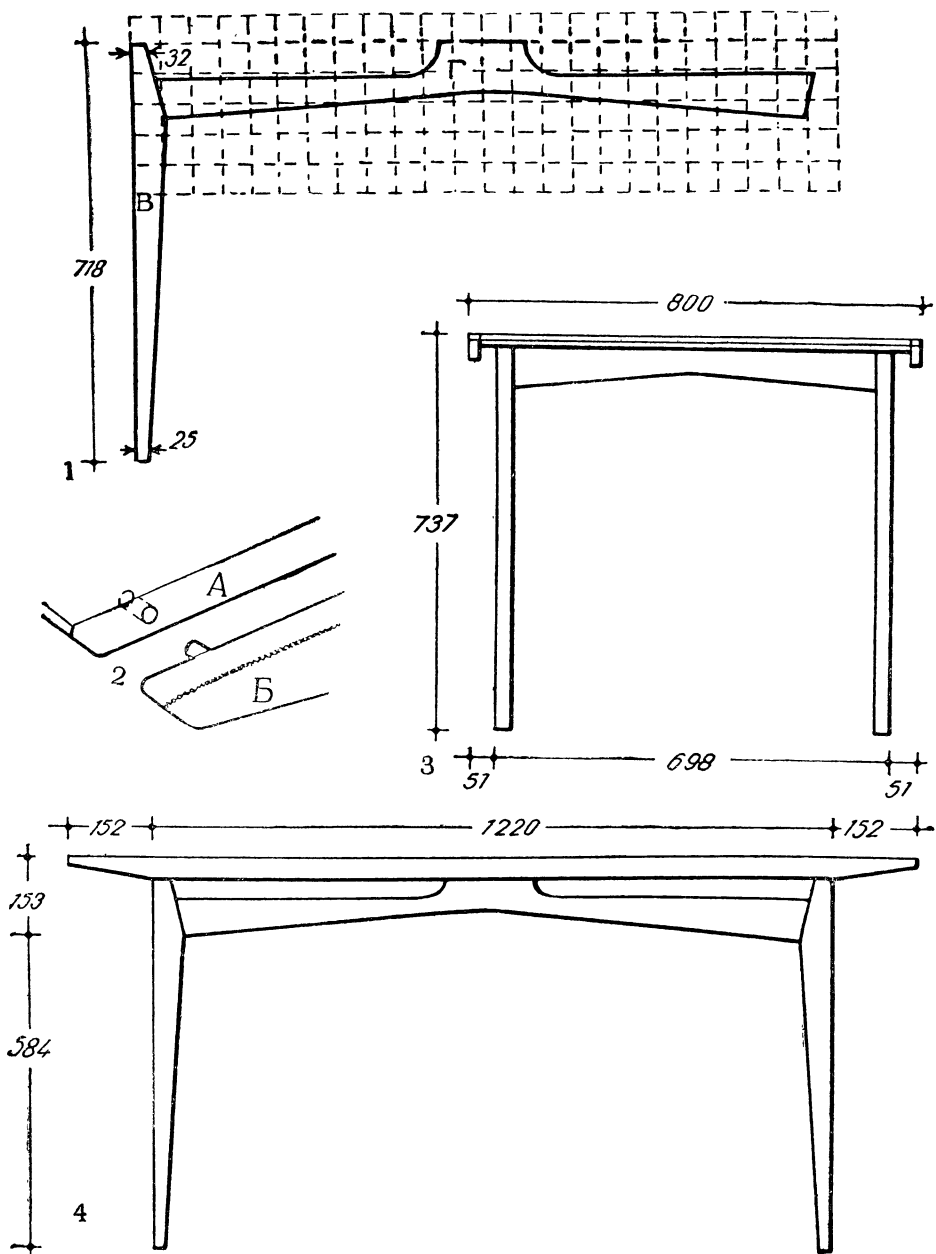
4. 1 — шаблон для изготовления ножек и царг (размер клетки — 50 мм); 2 — эскиз соединения крышки с обкладкой; 3 — вид сбоку; 4 — вид спереди.
